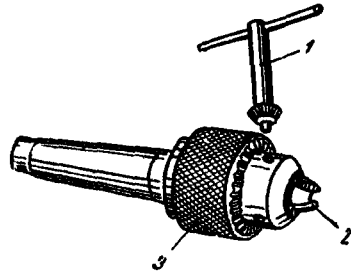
Трехкулачковый самоцентрирующий сверлильный патрон.
